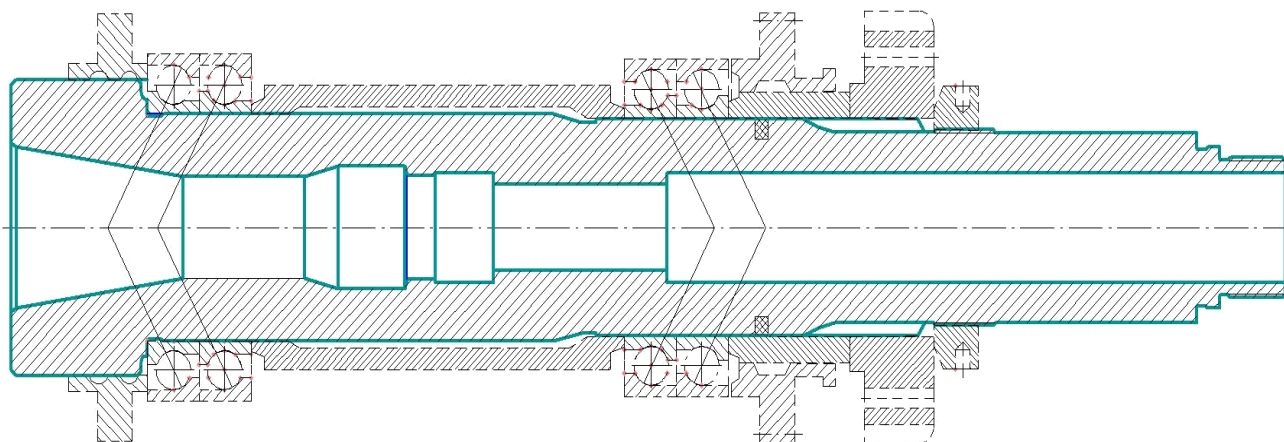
Конструктивная схема шпиндельного узла станка СФ68ВФ4
